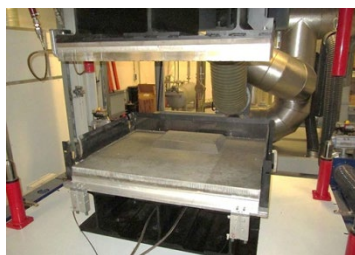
3D-Werkzeug für Faserblasprozess
